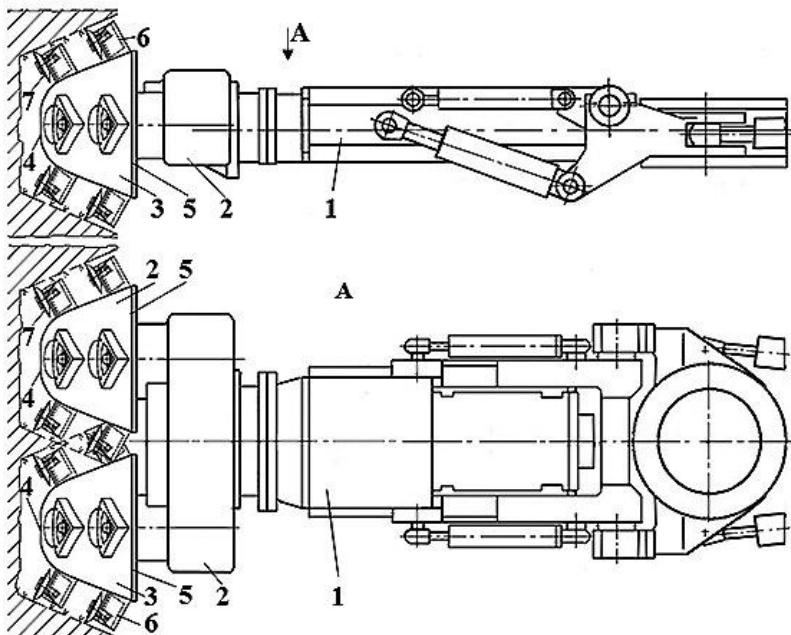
Конструкция исполнительного органа с двумя реверсивными коронками и дисками
